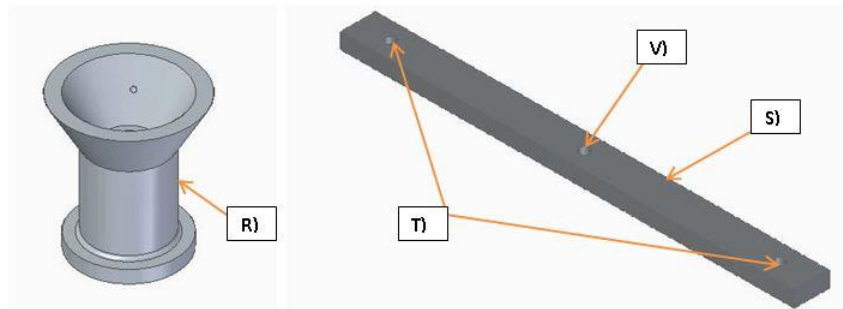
Uillaje travesaño nido bola. Nido central y travesaño.
